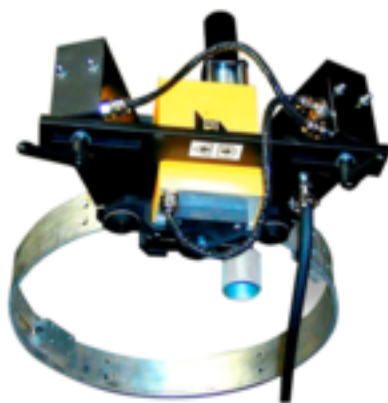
Сварочная головка Esab Railtrac Orbital [13]
